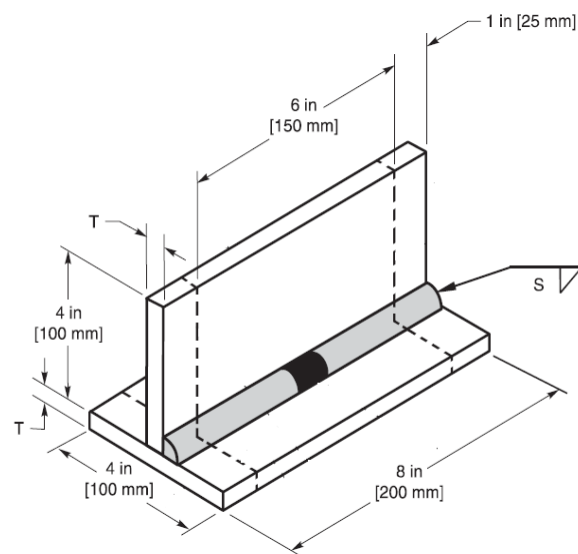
Probeta para calificación de rendimiento del soldador para soldadura en filete (welding, 2014)
